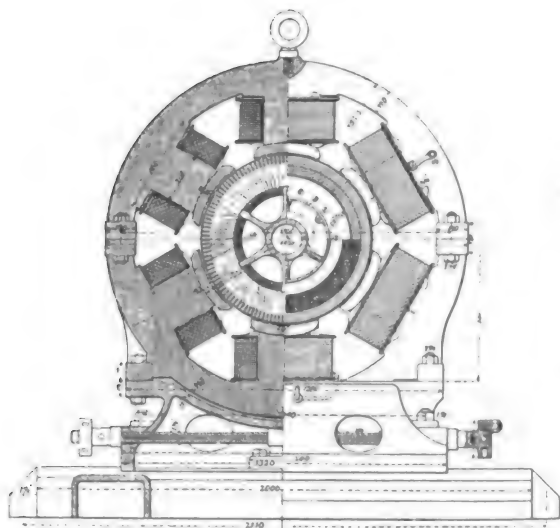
et 12. — Coupes d'une machine de 72 000 watts de la maison Willem Smit et Cie.
